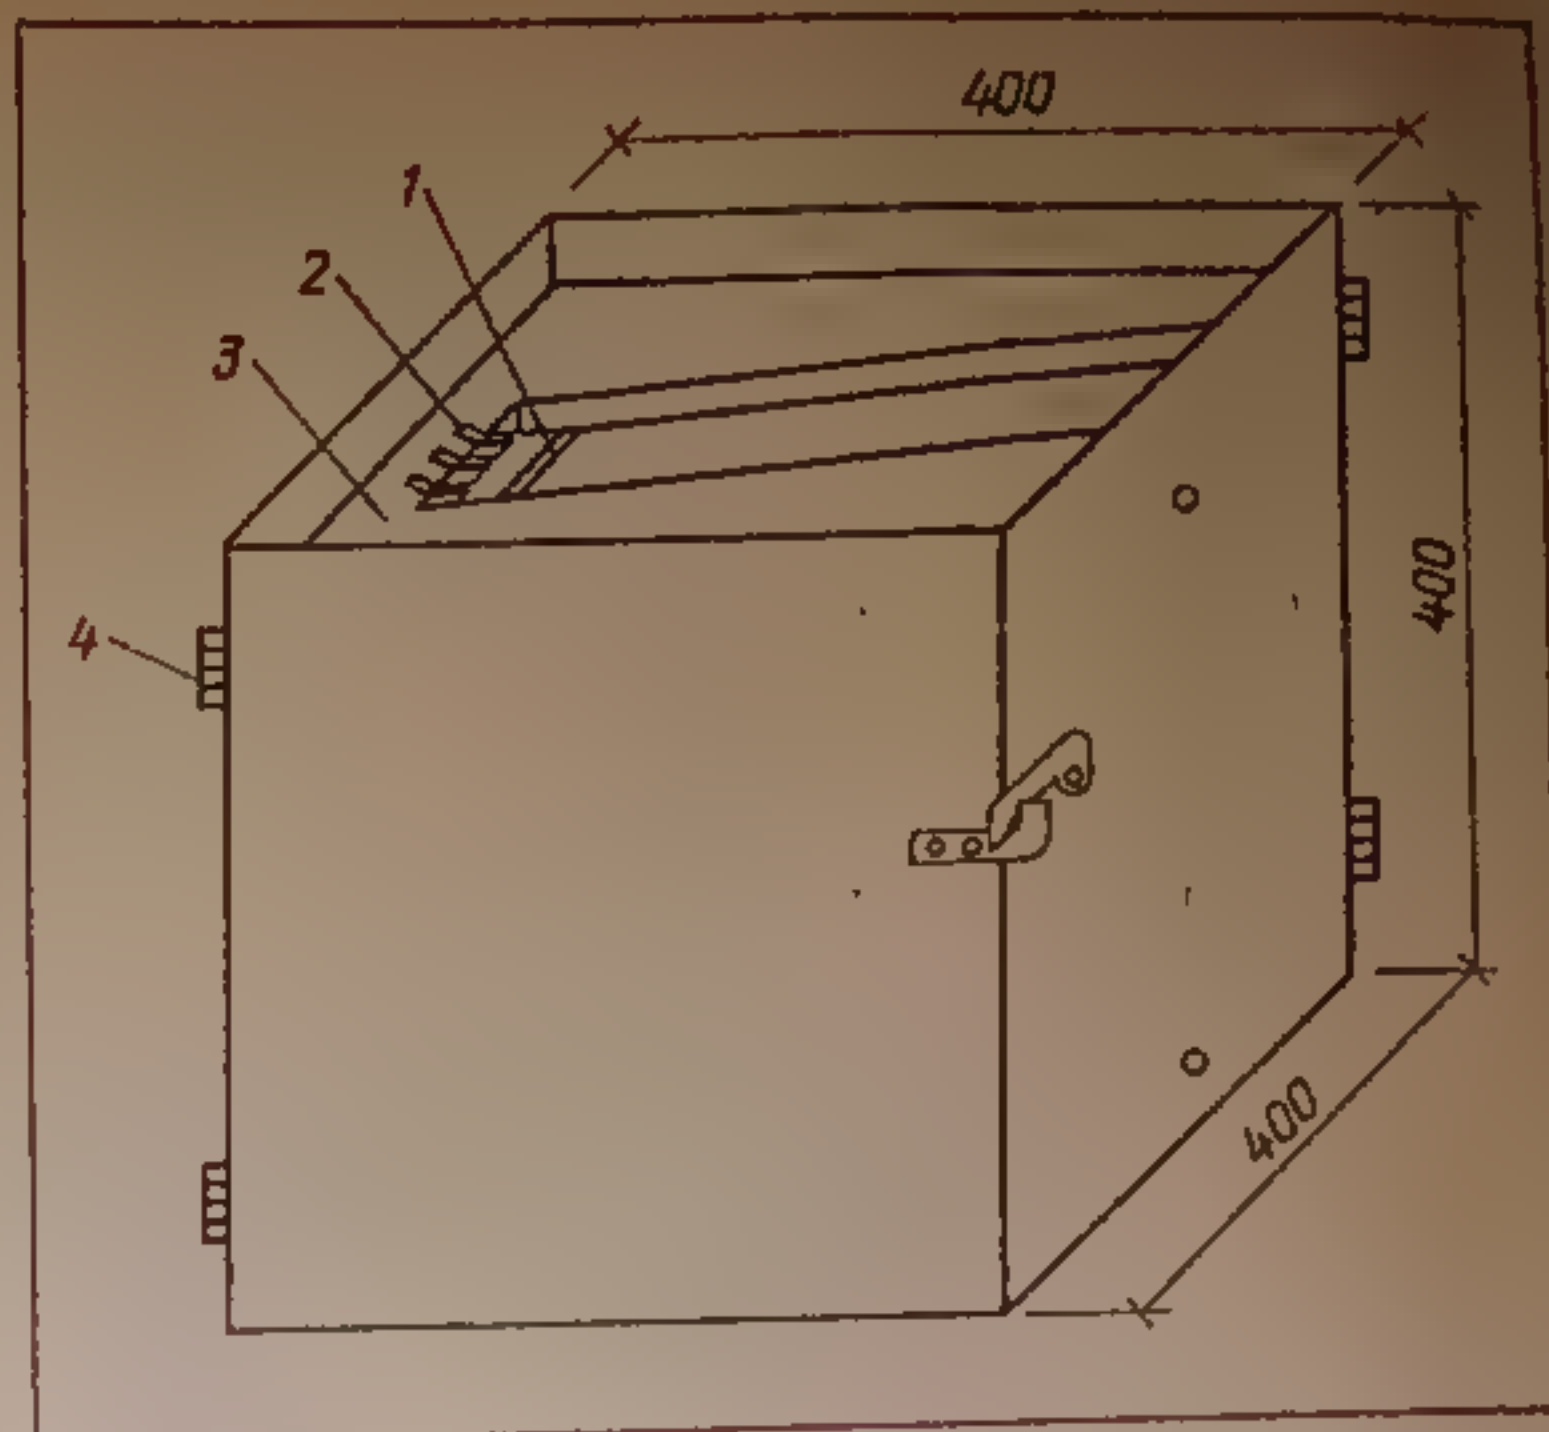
Шинковка-контейнер: 1 — уголок; 2 — прорезь для ножа; 3 — стол с отверстием; 4 — петля
